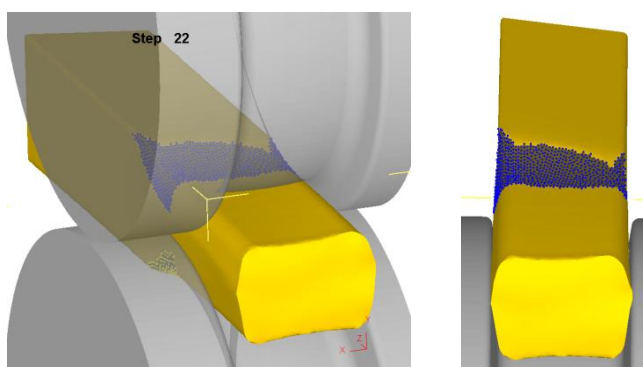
Точки контакта заготовки с поверхностью валка на стадии установившегося процесса прокатки заготовки с величиной ромбичности 20 мм и начальным углом поворота заготовки  $6^\circ$
